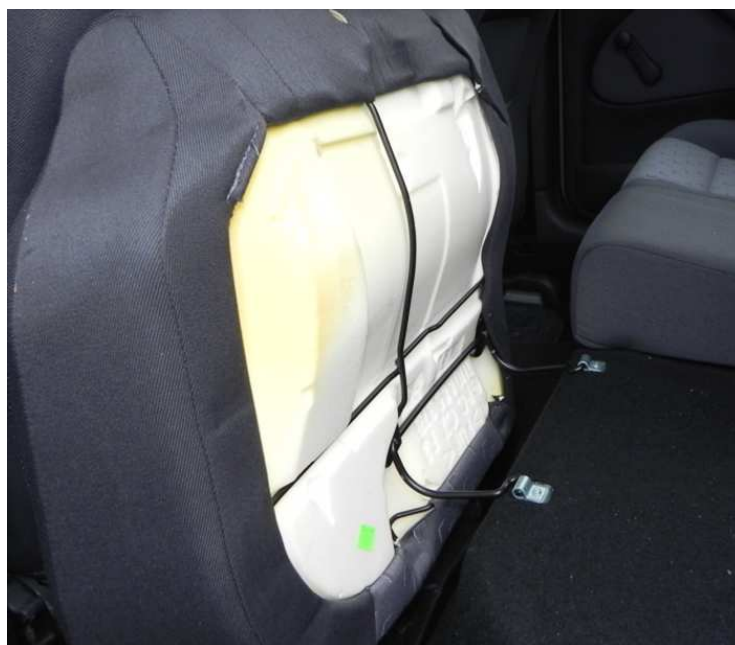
Upínací mechanismus zadní sedačky u vozu Superb
